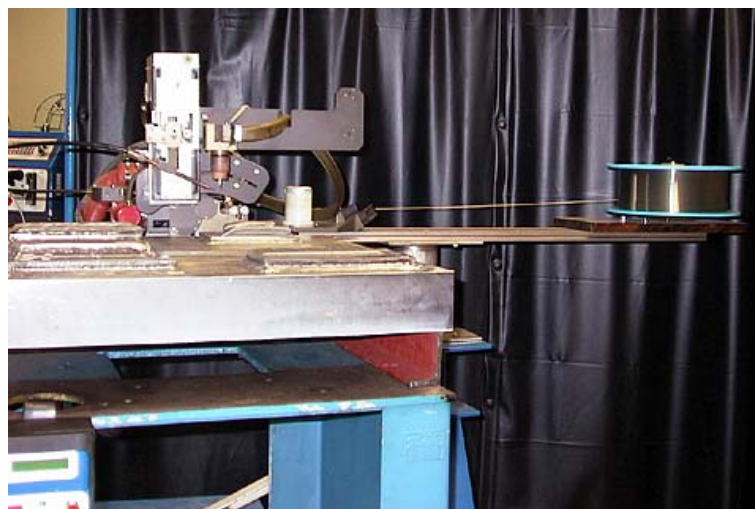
Versuchsanlage für das vollmechanisierte WIG-Kaltdraht-Auftragschweißen
